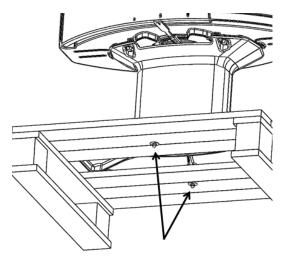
Particolare delle lamiere che fissano i piedi alla base di legno
